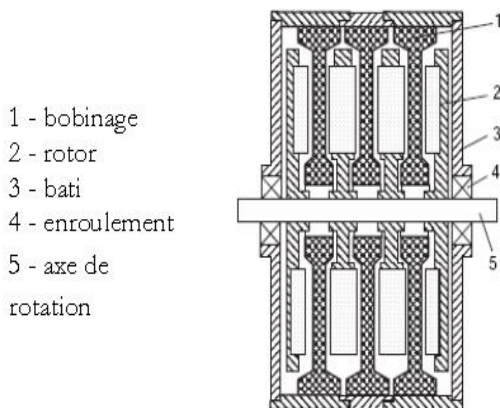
Descriptif de la machine à axial stator interne [16]
